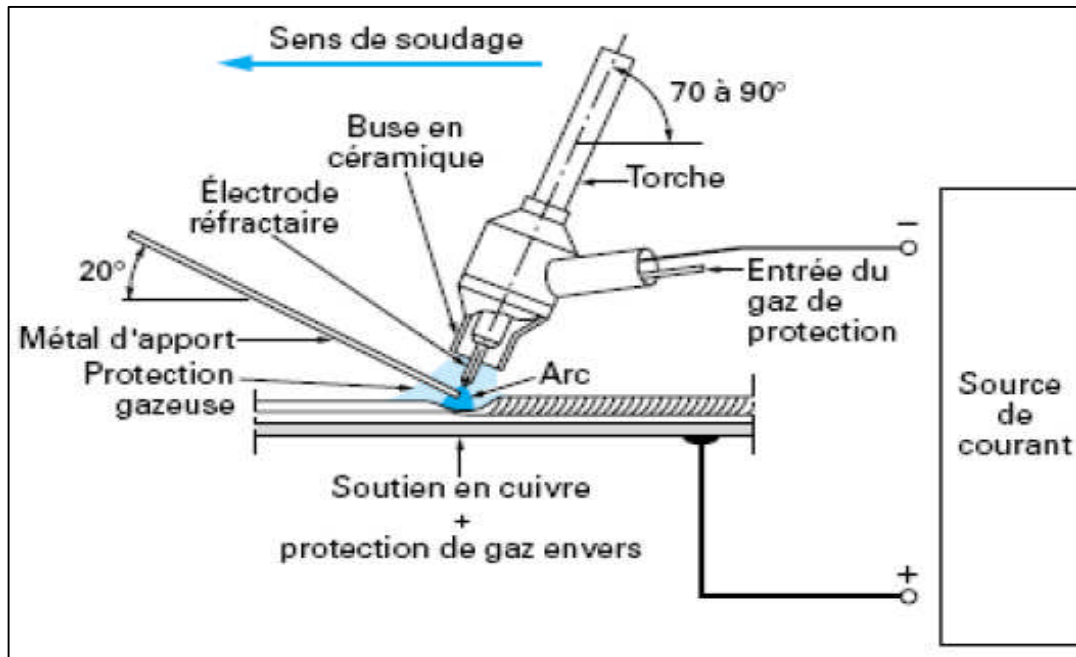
Principe du soudage manuel par le procédé TIG (ou GTAW) [27].
